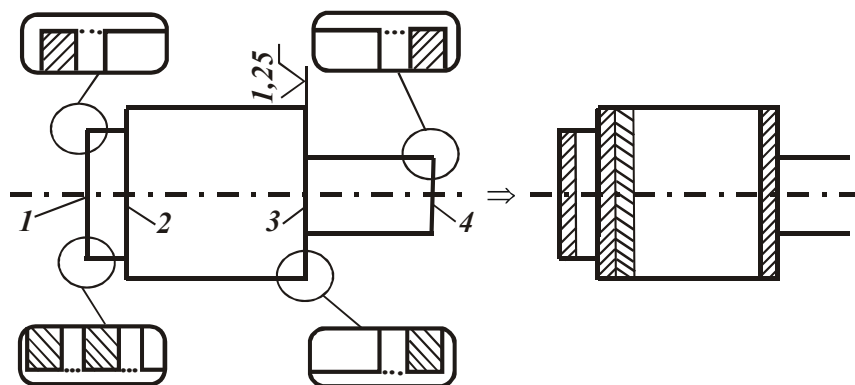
Схема анализа чертежа детали (заштрихованные участки – припуски); 1–4 – обрабатываемые поверхности.
